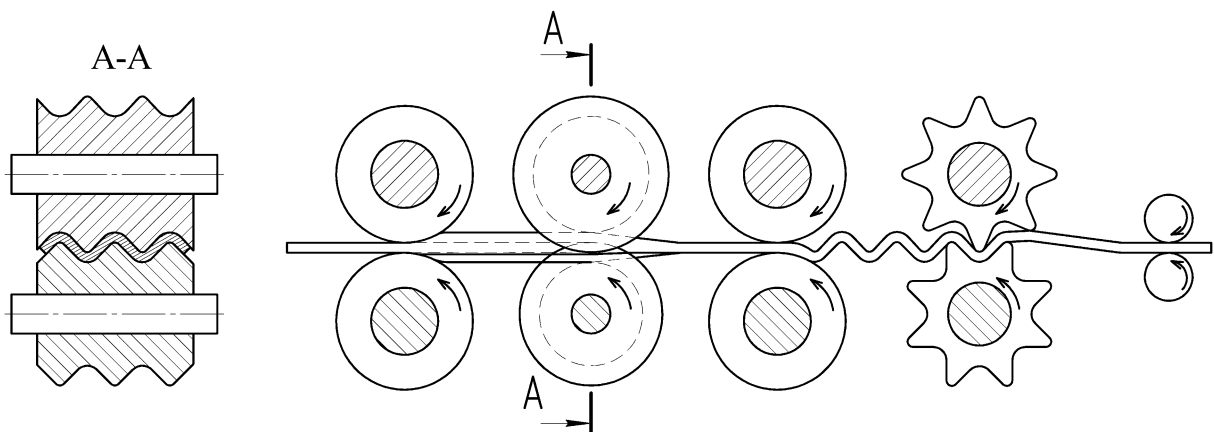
Схема процесса деформационного упрочнения листовой заготовки [1]
